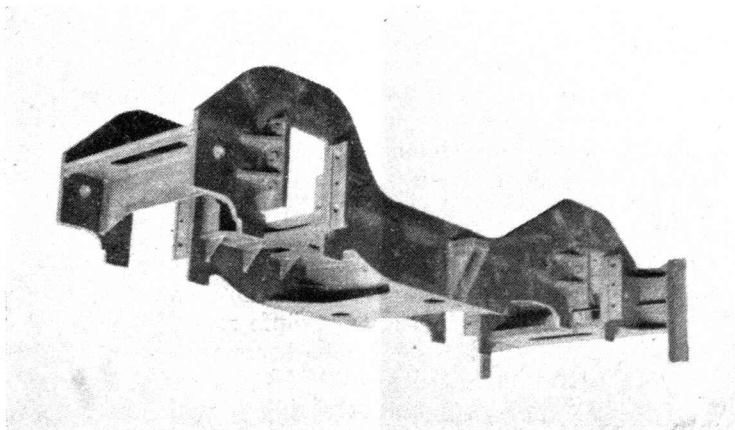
Geschweißter Drehgestellrahmen.
